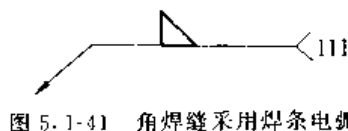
角焊缝采用焊条电弧焊
